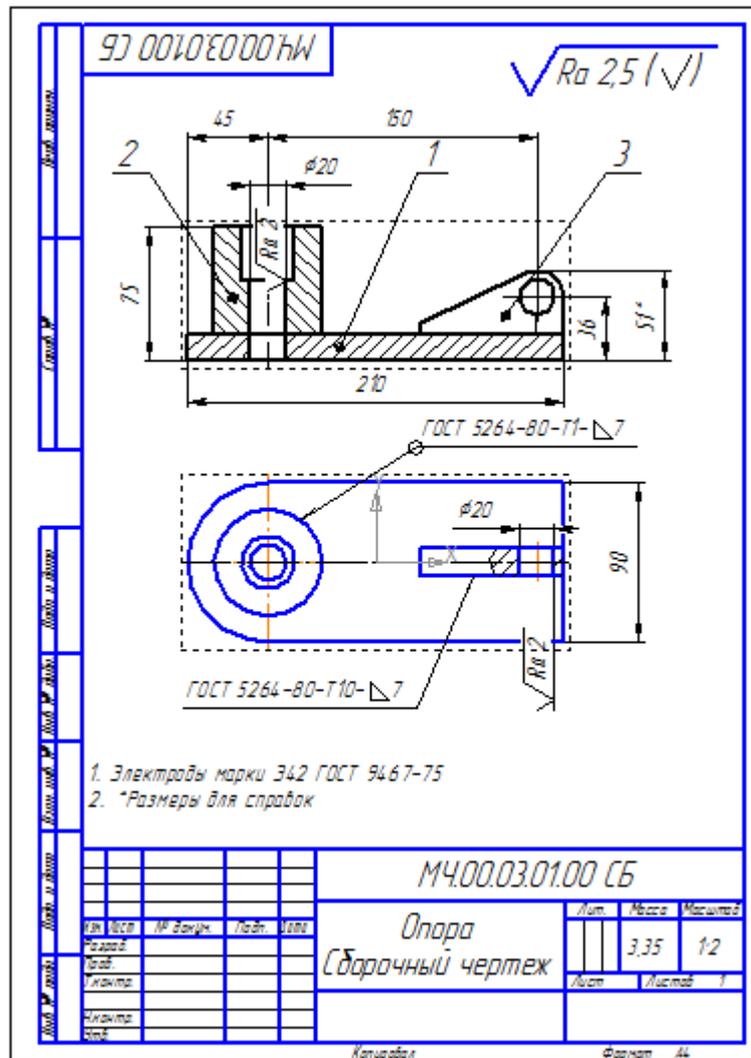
Пример выполнения на сборочный чертёж сварного изделия
